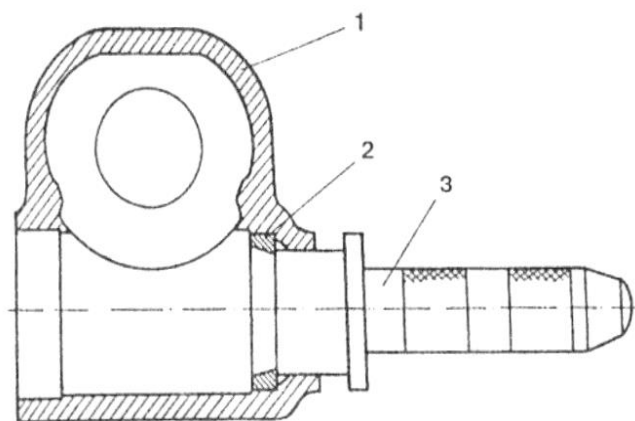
Снятие наружного кольца верхнего подшипника червяка с помощью оправки:
